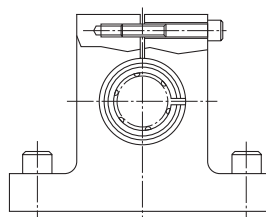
Ajuste del juego del rodamiento con un tornillo prisionero
